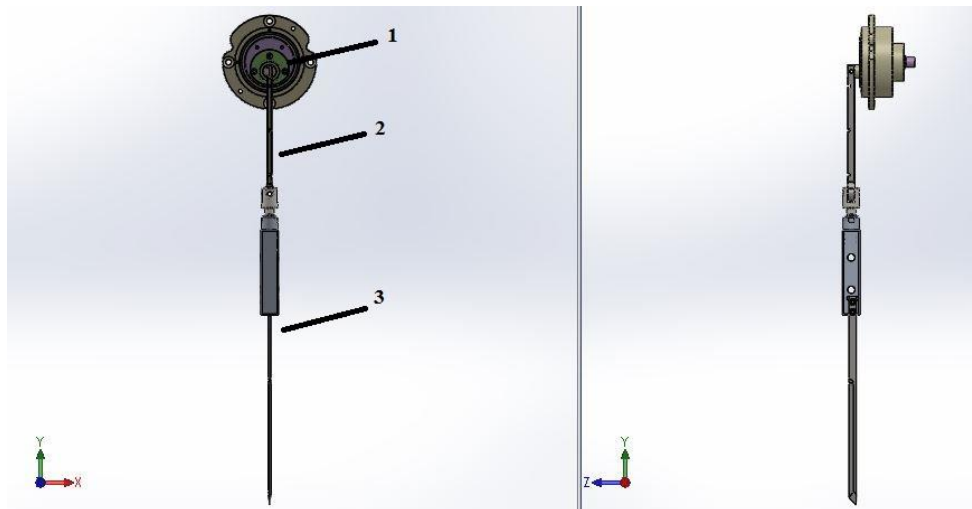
CNC Kesicinin hareket mekanizması (Movement mechanism of CNC Cutter)
